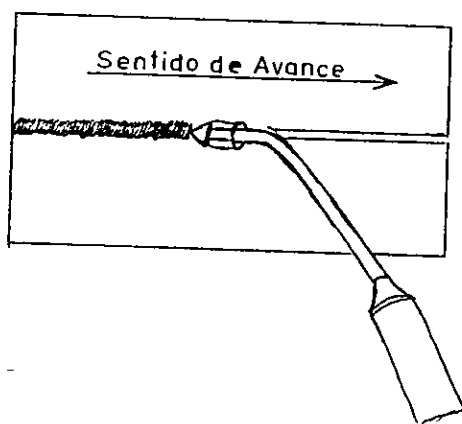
SOLDADURA A LA DERECHA O "ATRÁS"
